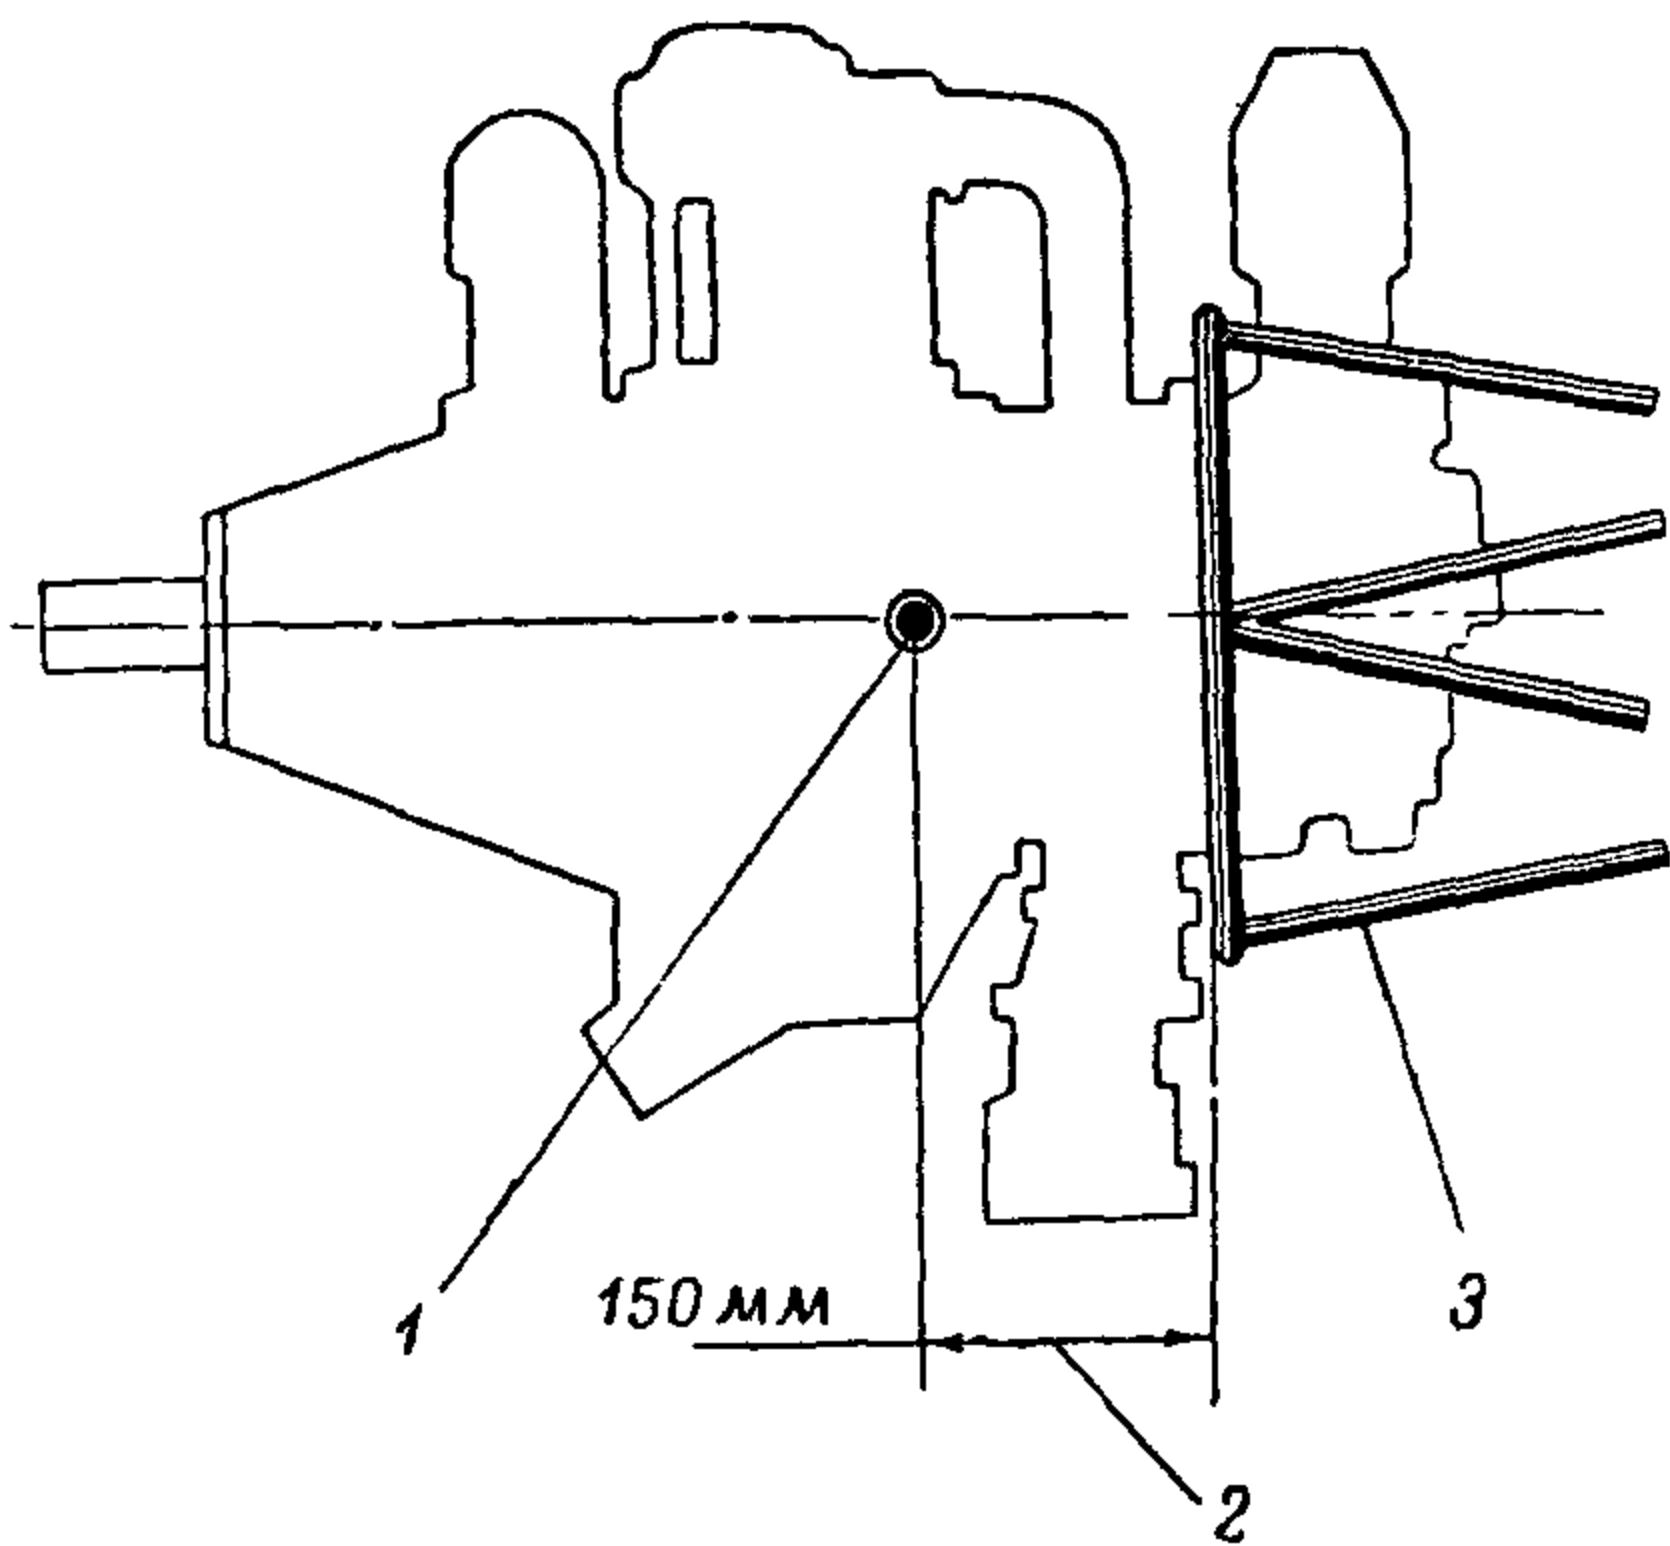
Схема расположения центра тяжести двигателя АИ-14Р
